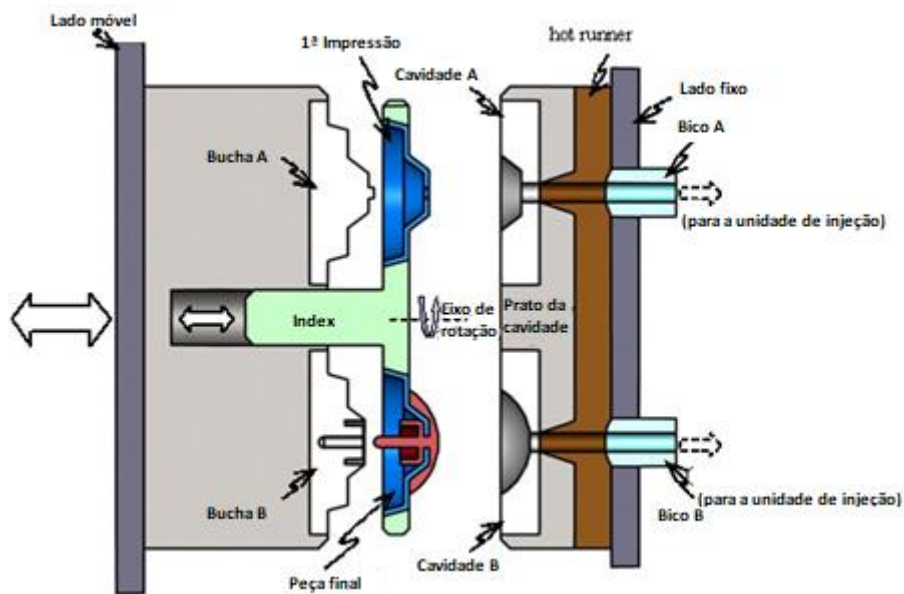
Mold e *index plate* e principais componentes. Adaptado de [23]
